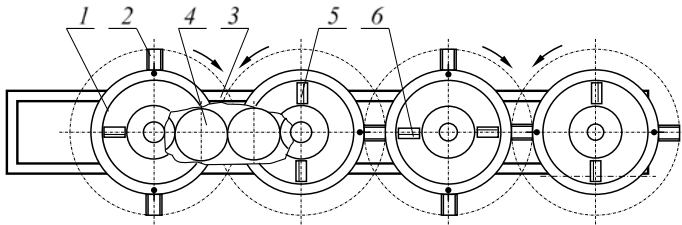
Режущий аппарат с роторами, имеющими радиальные прорези: 1 – роторы; 2 – ножи; 3 – корпус редуктора; 4 – шестерни; 5, 6 – радиальные прорези
